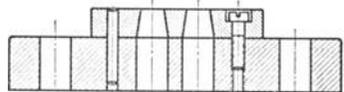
Befestigung der Schnittplatte durch Schrauben und Paßstifte.
